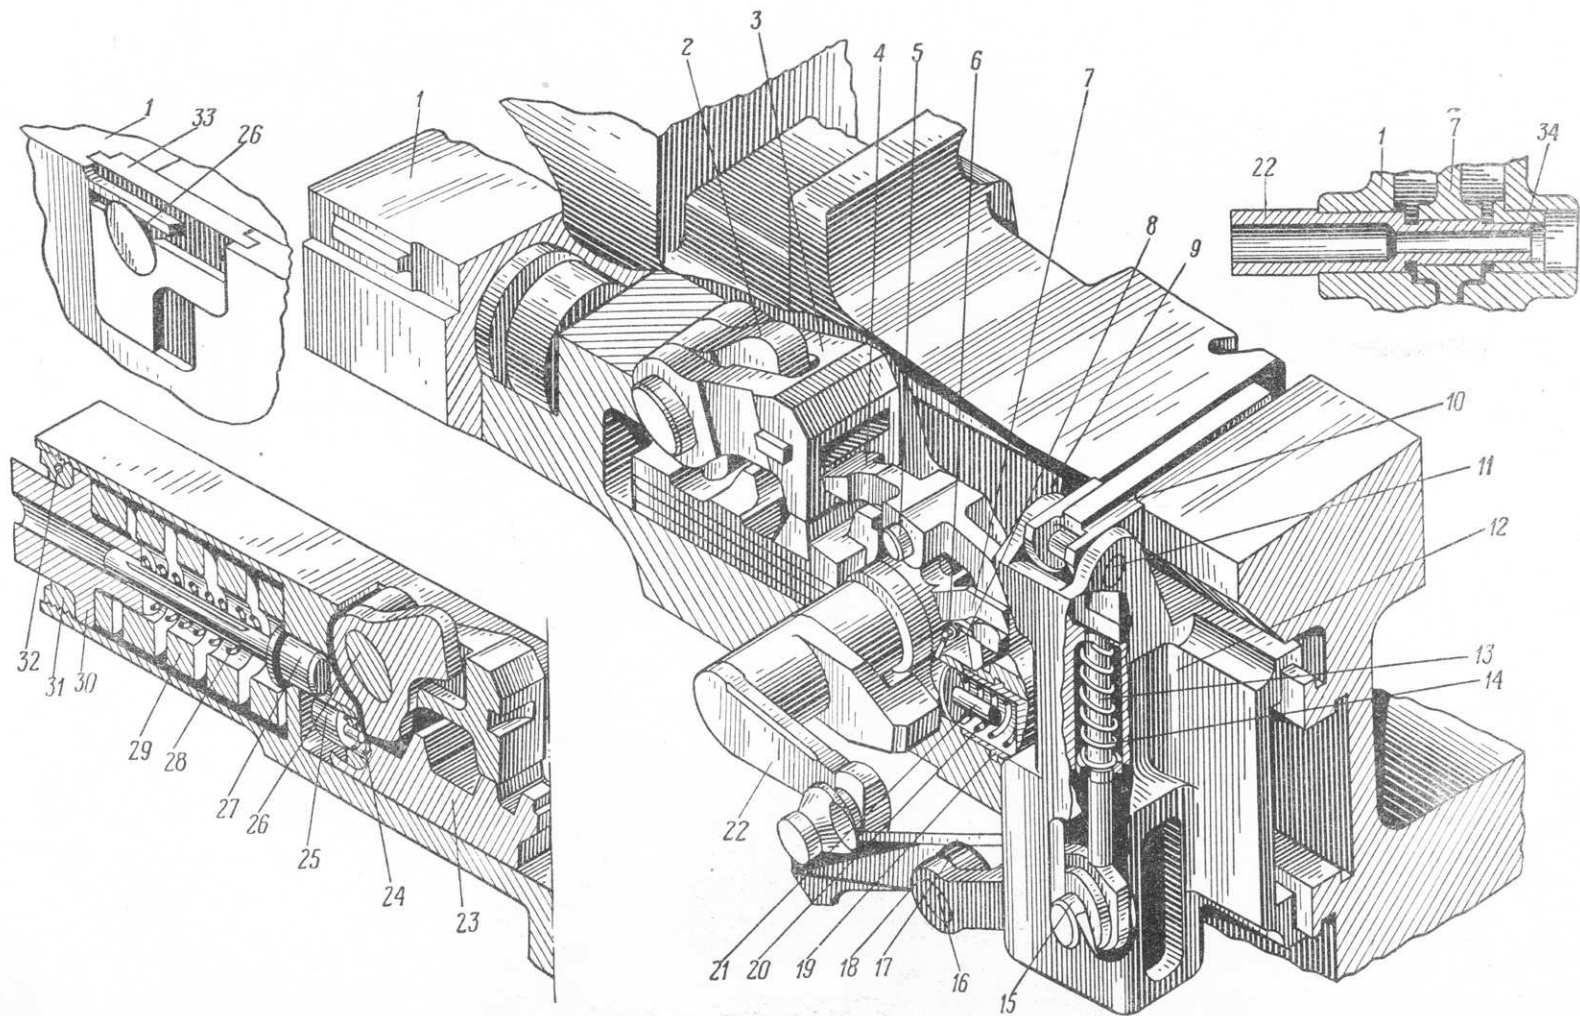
Спусковой механизм левого автомата (разрез):
